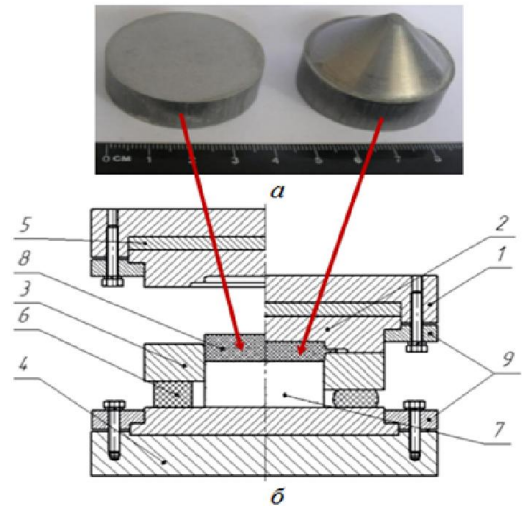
Зовнішній вигляд заготовок під штамповку (а) та експериментальний штамп для гарячого пресування (б)
